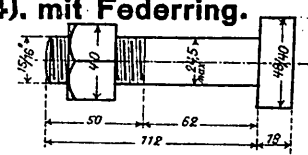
Laschenschraube Form A (1:4), mit Federring.
